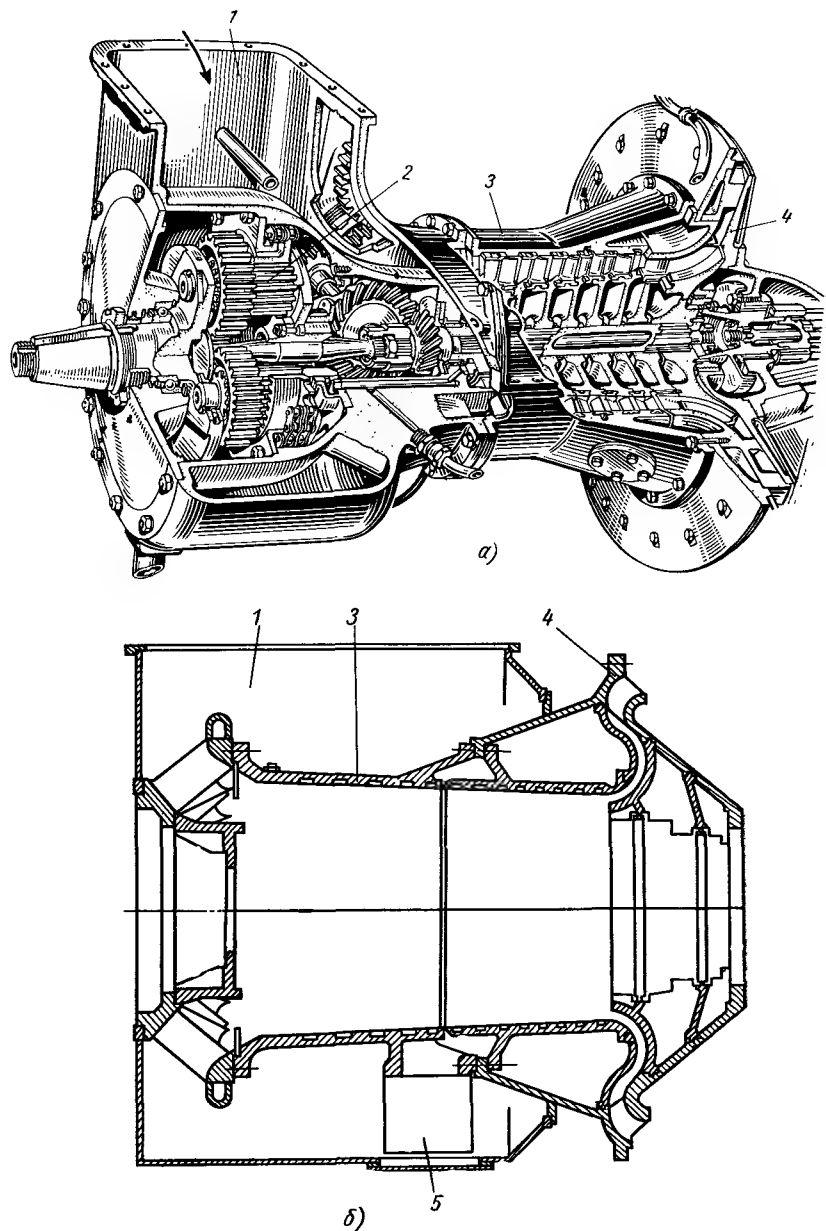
Компрессор с одностенным корпусом в части низкого давления и двухстенным в части высокого давления:
